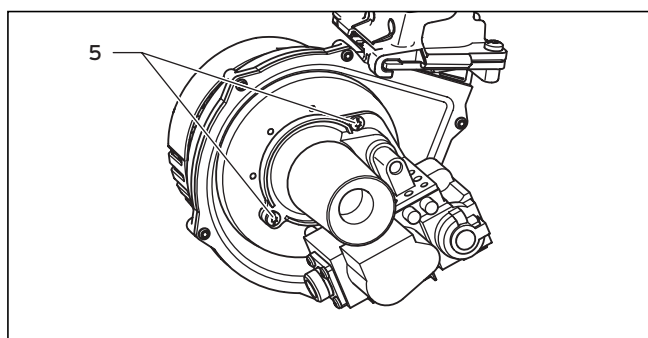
Резьбовое соединение газовая арматура/вентилятор
